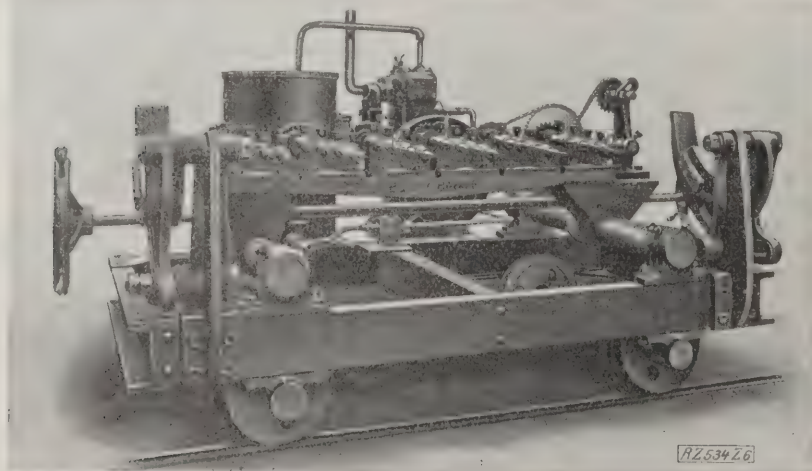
Mastenanstechmaschine von Becker mit Antrieb durch Benzinmotor.
